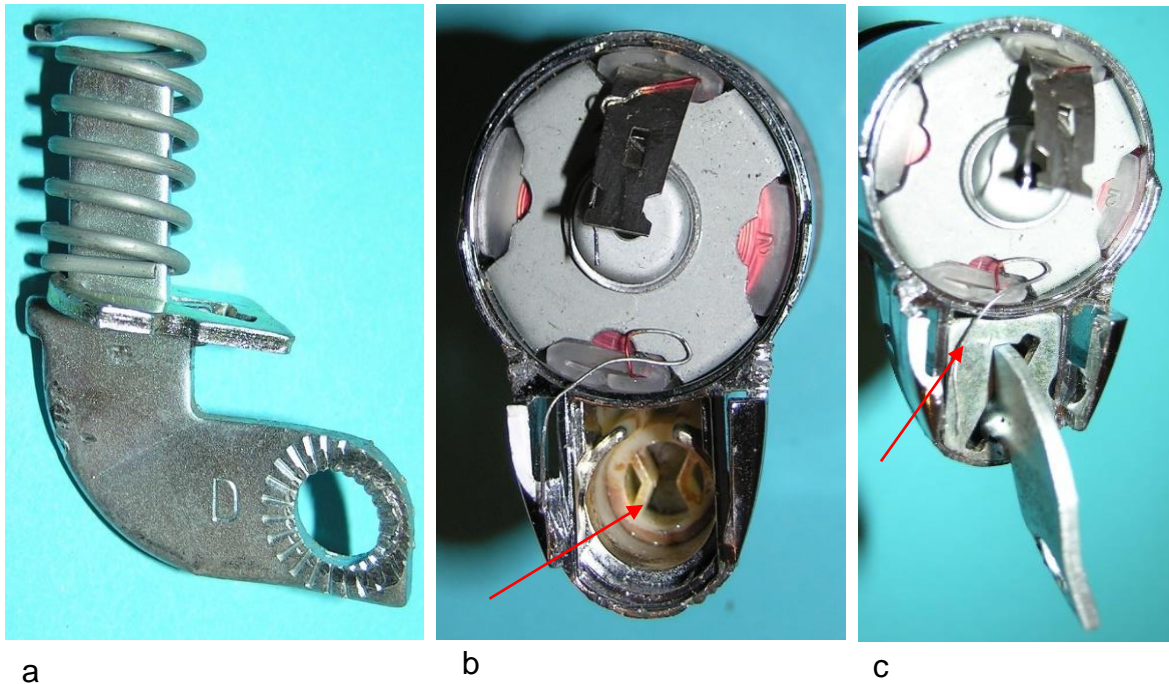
Montage der Kippvorrichtung: a) Drehbolzen mit Halterarm, Kulissenblech und Druckfeder, b) Führungselement in der Gehäusekammer, c) Position des Kulissenplatte im Gehäuse
